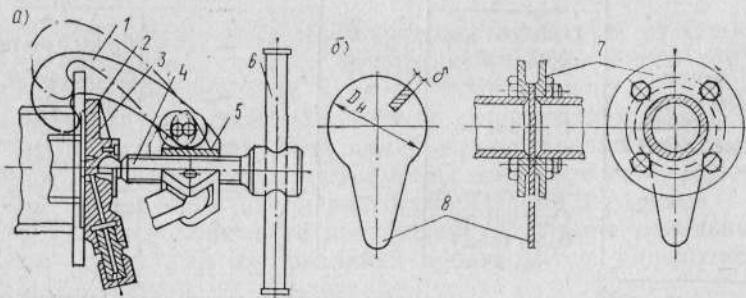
Заглушка для испытаний трубопроводов с фланцами
